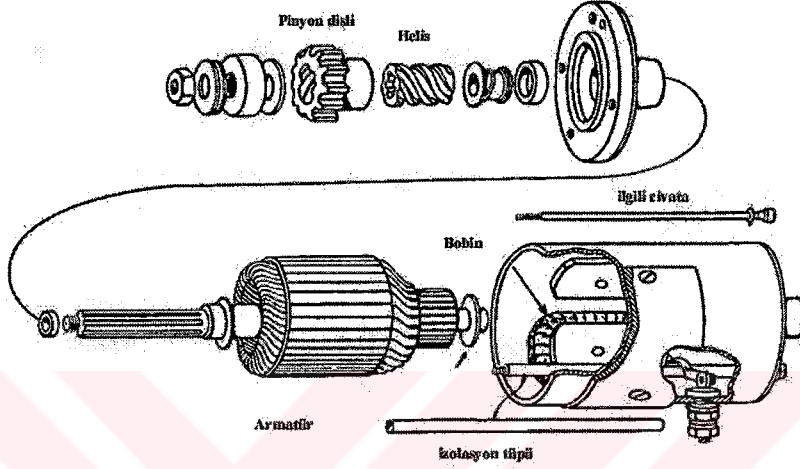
Elektrikli ilk hareket düzeneđi (Miller & Miller, 1993)
